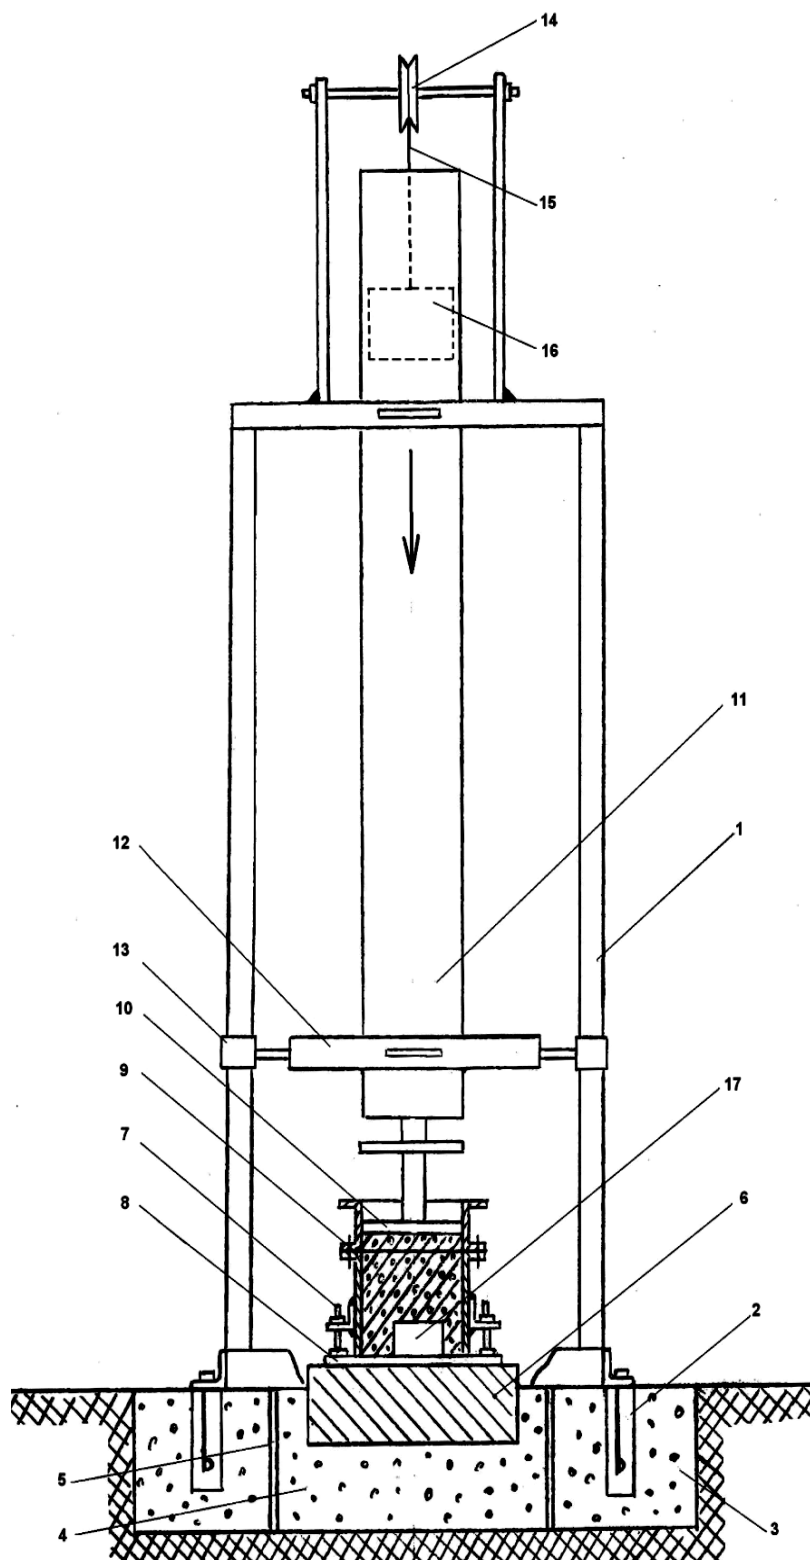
Лабораторная установка для ВСП с падающим грузом, авторы Ильных Е. С., Москалев В. Г.: 1 – станина; 2 – анкерный болт; 3 – обычный фундамент; 4 – армированный фундамент; 5 – деревянная опалубка; 6 – ударник; 7 – болт; 8 – подмодельная плита; 9 – опока; 10 – плунжер; 11 – направляющая труба; 12 – каретка; 13 – ползун; 14 – шкив; 15 – трос; 16 – наборный груз; 17 – модель
